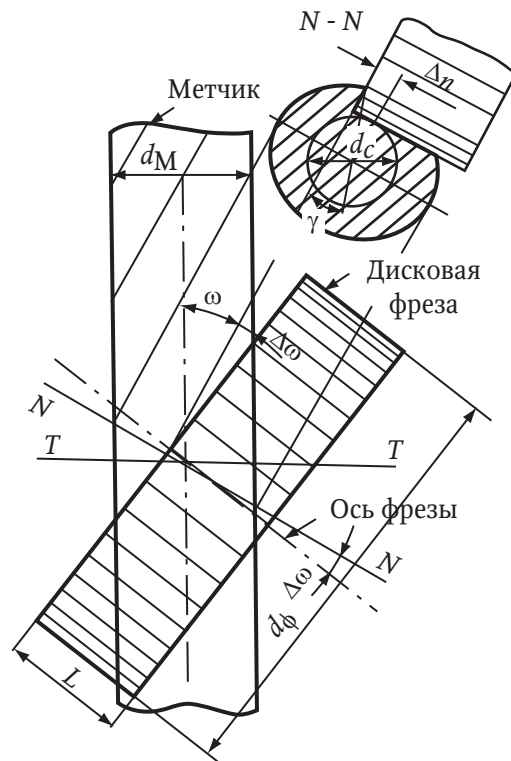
Схема фрезерования стружечных канавок дисковой трехсторонней фрезой
